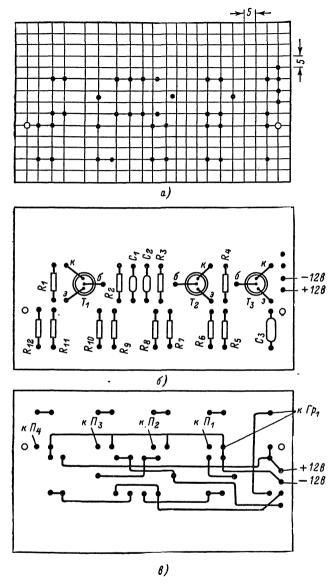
Размерка платы (a) и монтаж деталей на ней (6 и  $\theta)$ .
